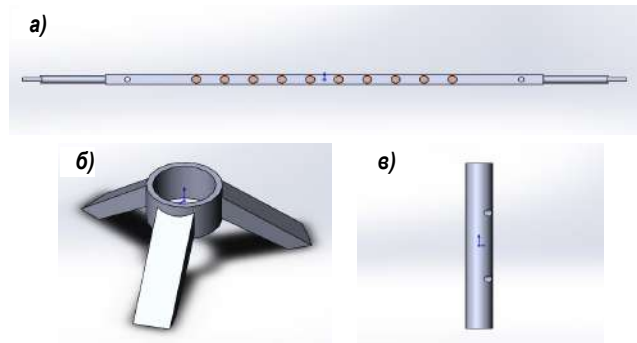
Детали дефектоскопа: а – опора для ультразвуковых датчиков, б – основа толщиномера, в – стойка
